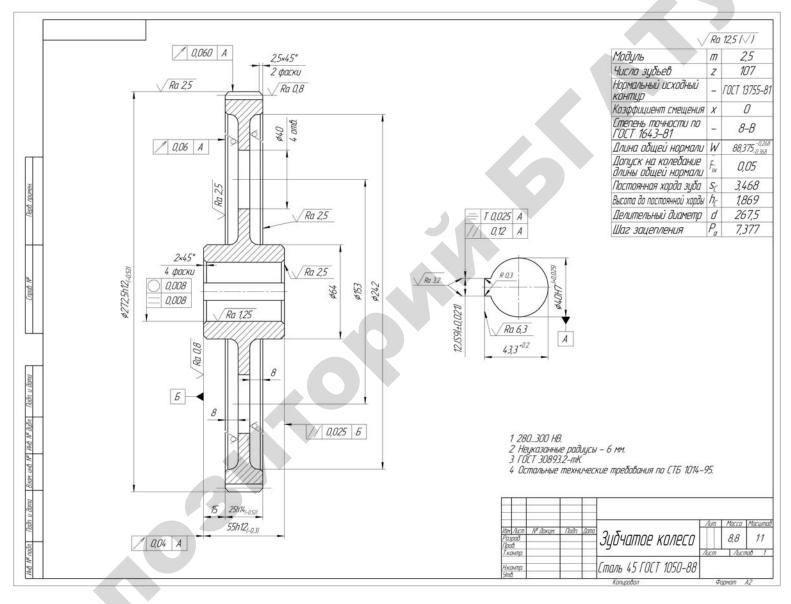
Пример выполнения чертежа цилиндрического зубчатого колеса
